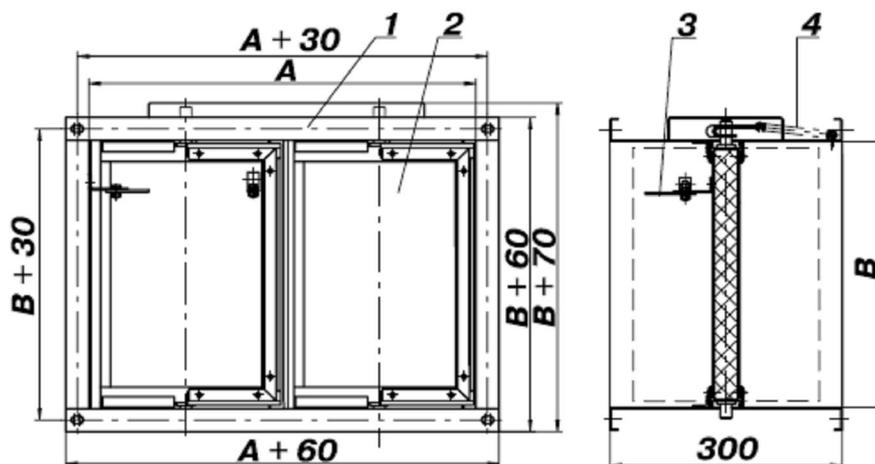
Прямоугольный клапан с плавким предохранителем и возвратной пружиной: 1 – корпус; 2 – лопатка; 3 – плавкая вставка; 4 – пружина
